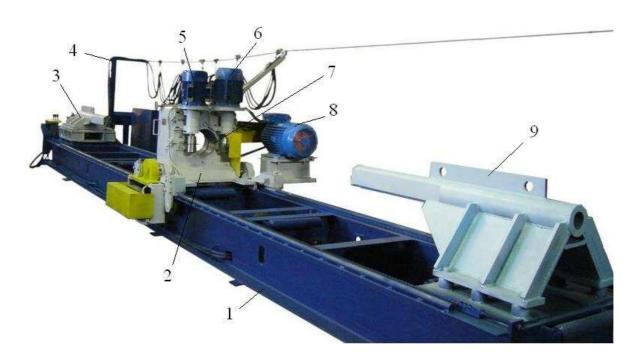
Станок оцилиндровочный «Шервуд ОФ-40Ц»:
